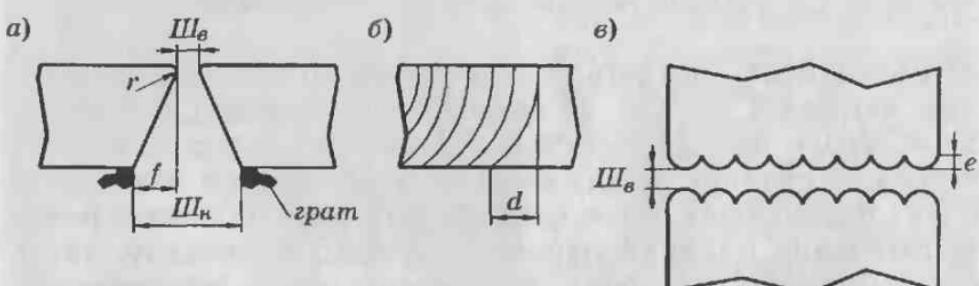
Параметры реза: а — поперечное сечение реза; б — поверхность кромки внутри реза; в — вид реза сверху;
